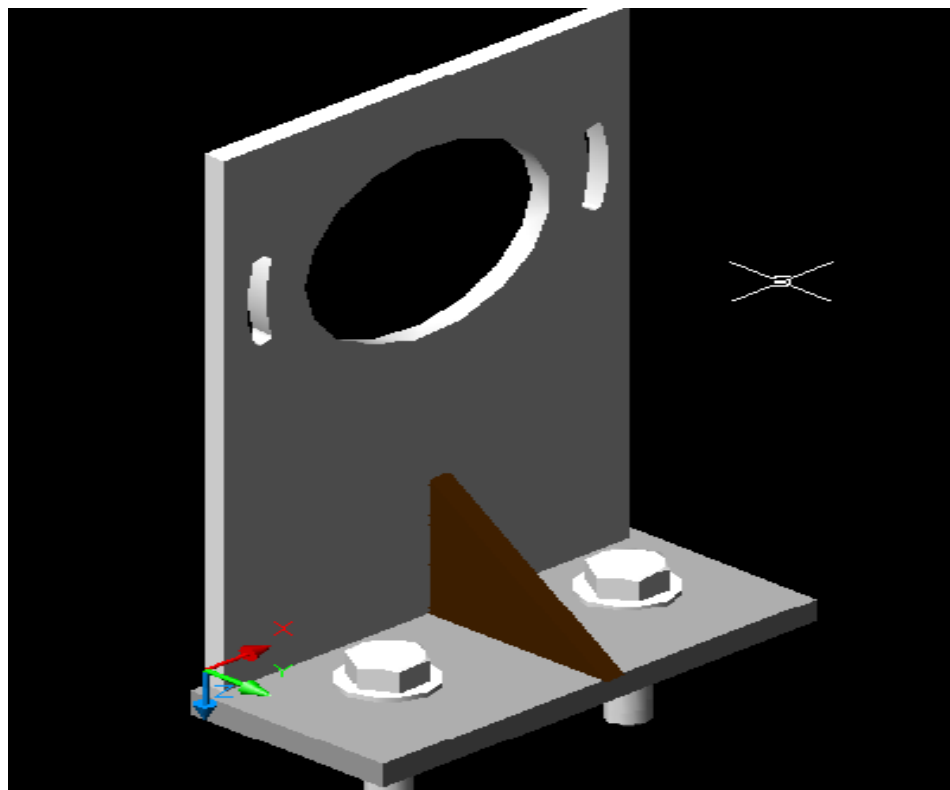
Vista isométrica 3 de la Placa que soporta el motor de arranque
